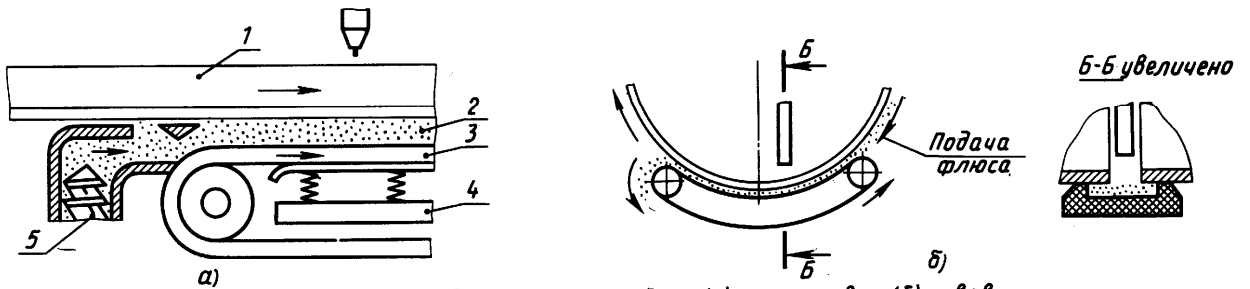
Флюсоремная подушка для сварки прямолинейных (а) и кольцевых (б) швов
